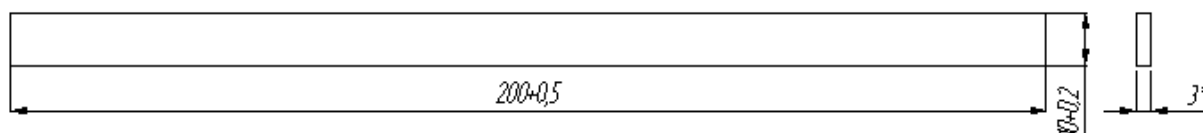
Образец для испытаний на растяжение, ГОСТ 32656 [2]
